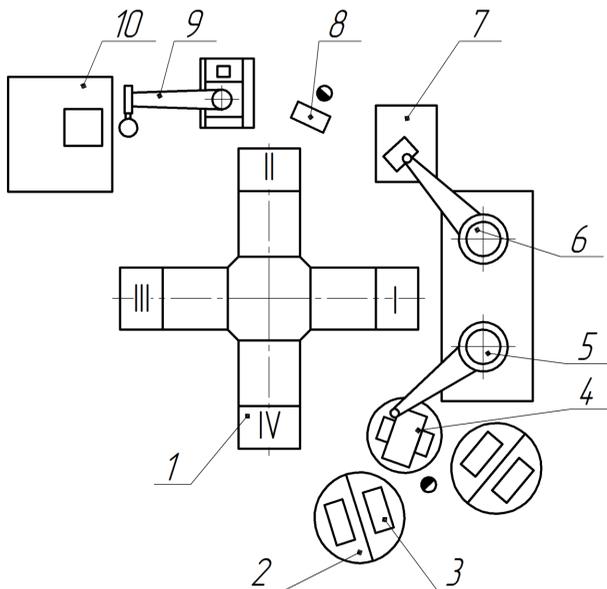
Роботизированный комплекс кокильного литья: 1 – карусельная четырехпозиционная установка кокильного литья; 2, 4, 7 – столы; 3 – контейнер; 5, 6 – промышленные роботы; 8 – пульт управления РТК; 9 – автооператор для заливки форм; 10 – раздаточная печь
